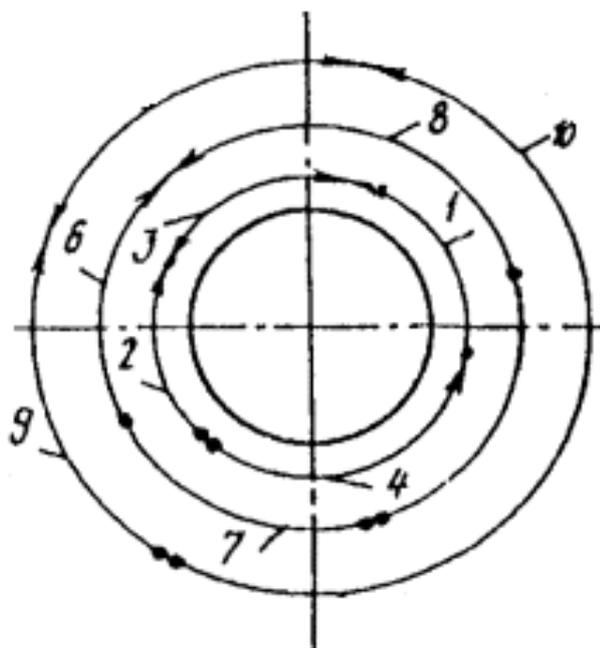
Схема наложения слоев при сварке неповоротных стыков труб диаметров от 300 мм
